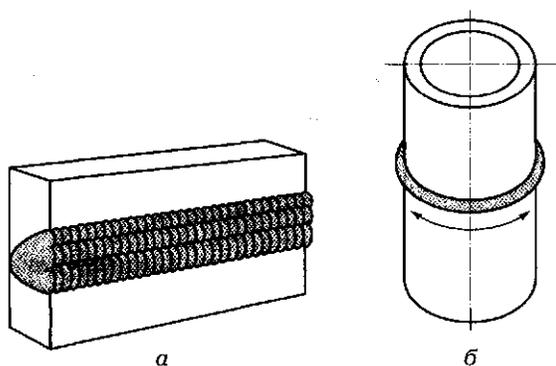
Положение при сварке стыковых швов:
